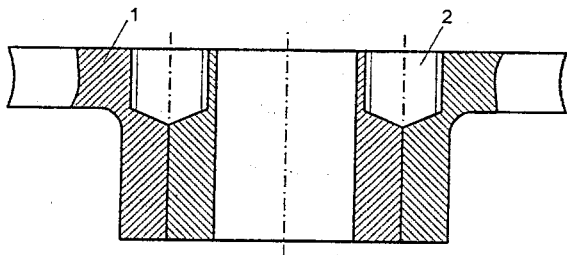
Ремонт посадочної поверхні підшипникового щита:
